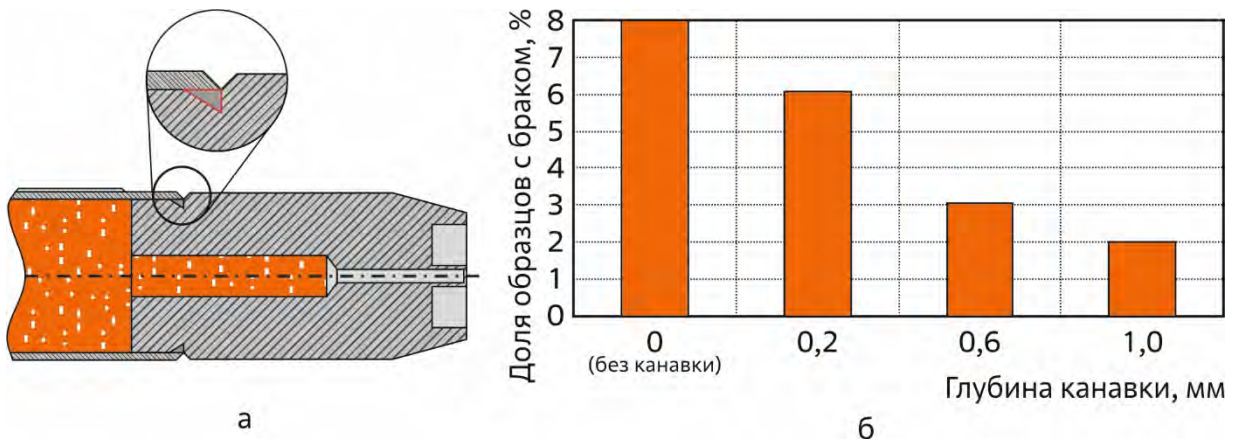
Конструкция сварного соединения с канавкой (а) и влияние её глубины на количество дефектов (б)
